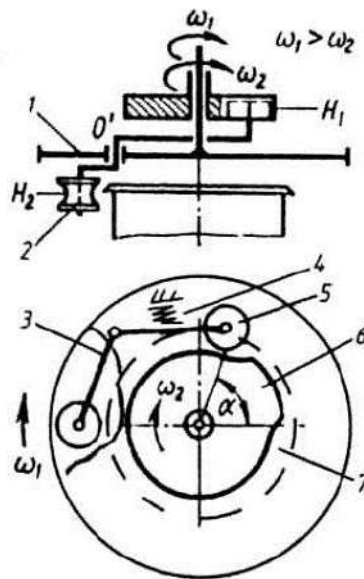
Схема закатувального механізму одношпindelного напівавтомата:
